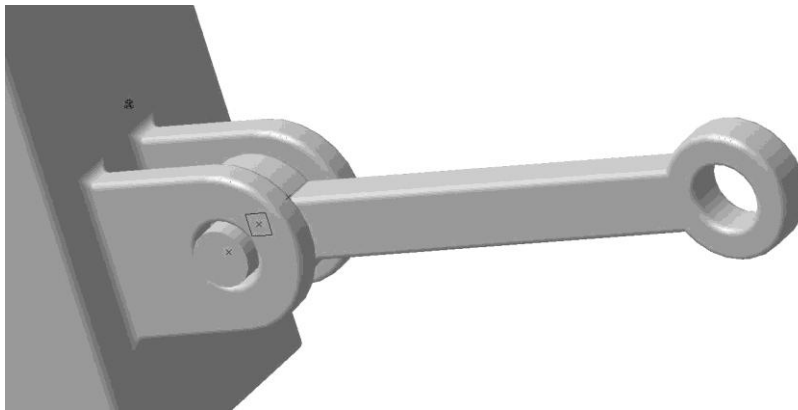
Anclaje para el tirante del sistema de bieletas
